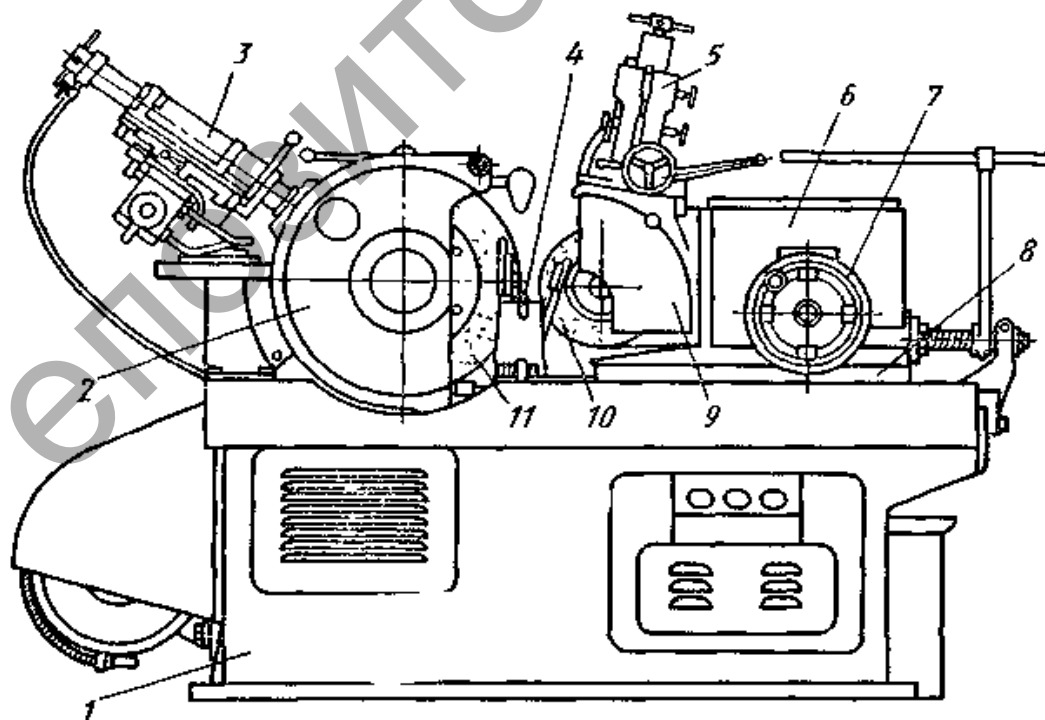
Бесцентровый круглошлифовальный станок
